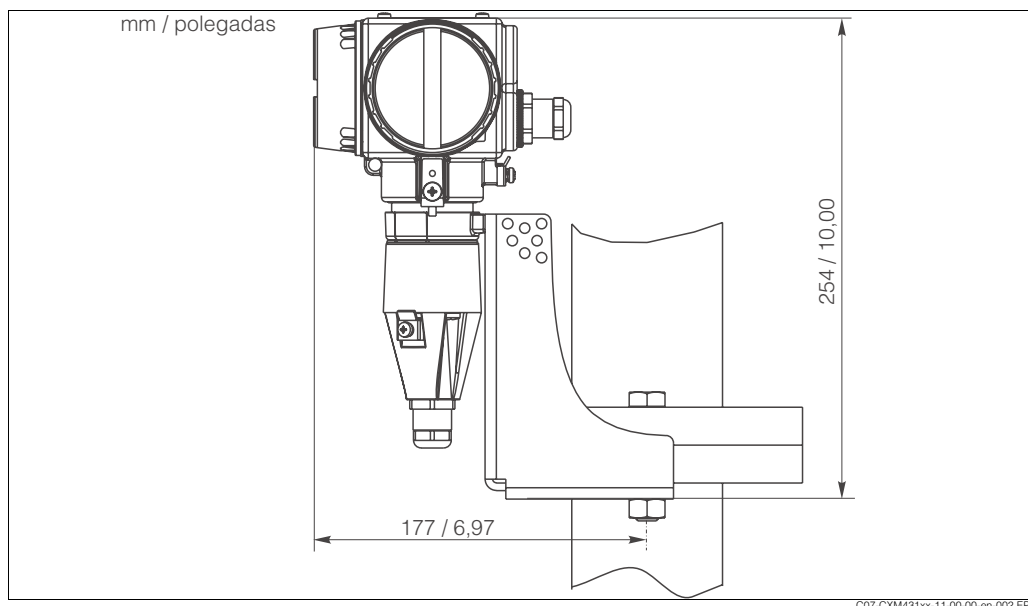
MyPro: Instalação de flange com suporte para montagem (com CXM431-xxx4xx no escopo de entrega)
